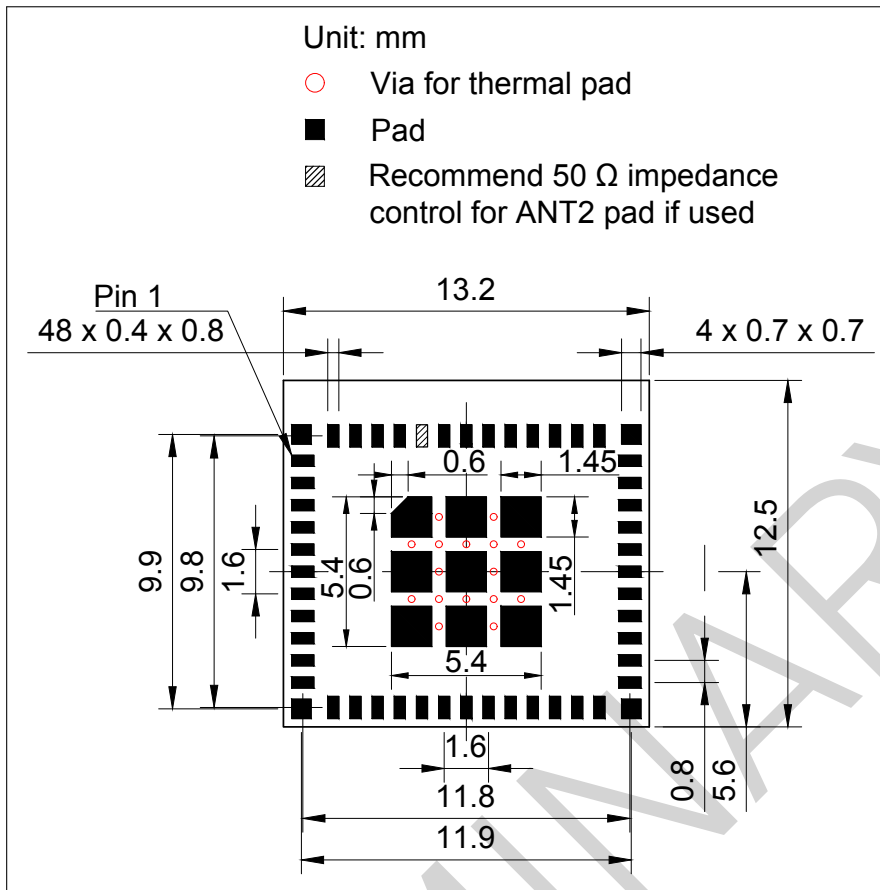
ESP32-C61-MINI-1U 推荐 PCB 封装图形
